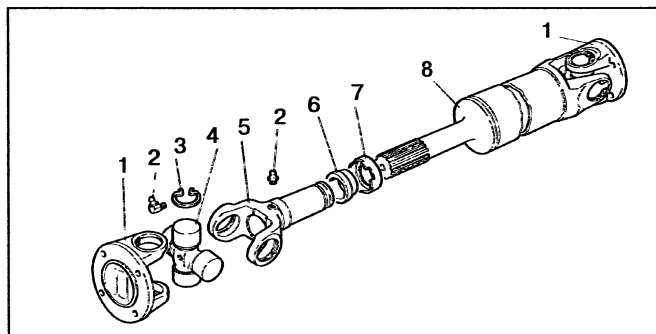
Детали переднего карданного вала: 1 – фланец-вилка карданного шарнира; 2 – пресс-масленка; 3 – стопорное кольцо; 4 – крестовина в сборе; 5 – скользящая вилка; 6 – сальник; 7 – обойма сальника; 8 – карданный вал
